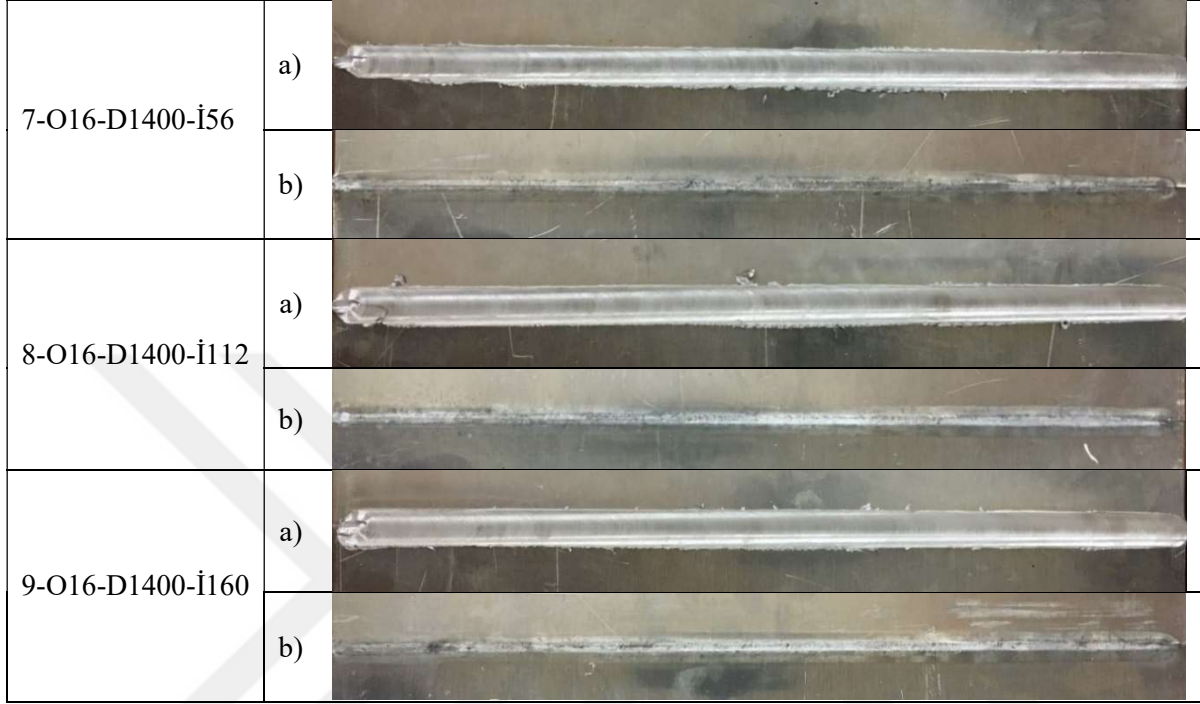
16 mm takım omuz çapı ve 710 dev/dk. takım dönme hızında elde edilen kaynaklı numuneler a) Kaynak yüzeyi, b) Kaynak kökü
